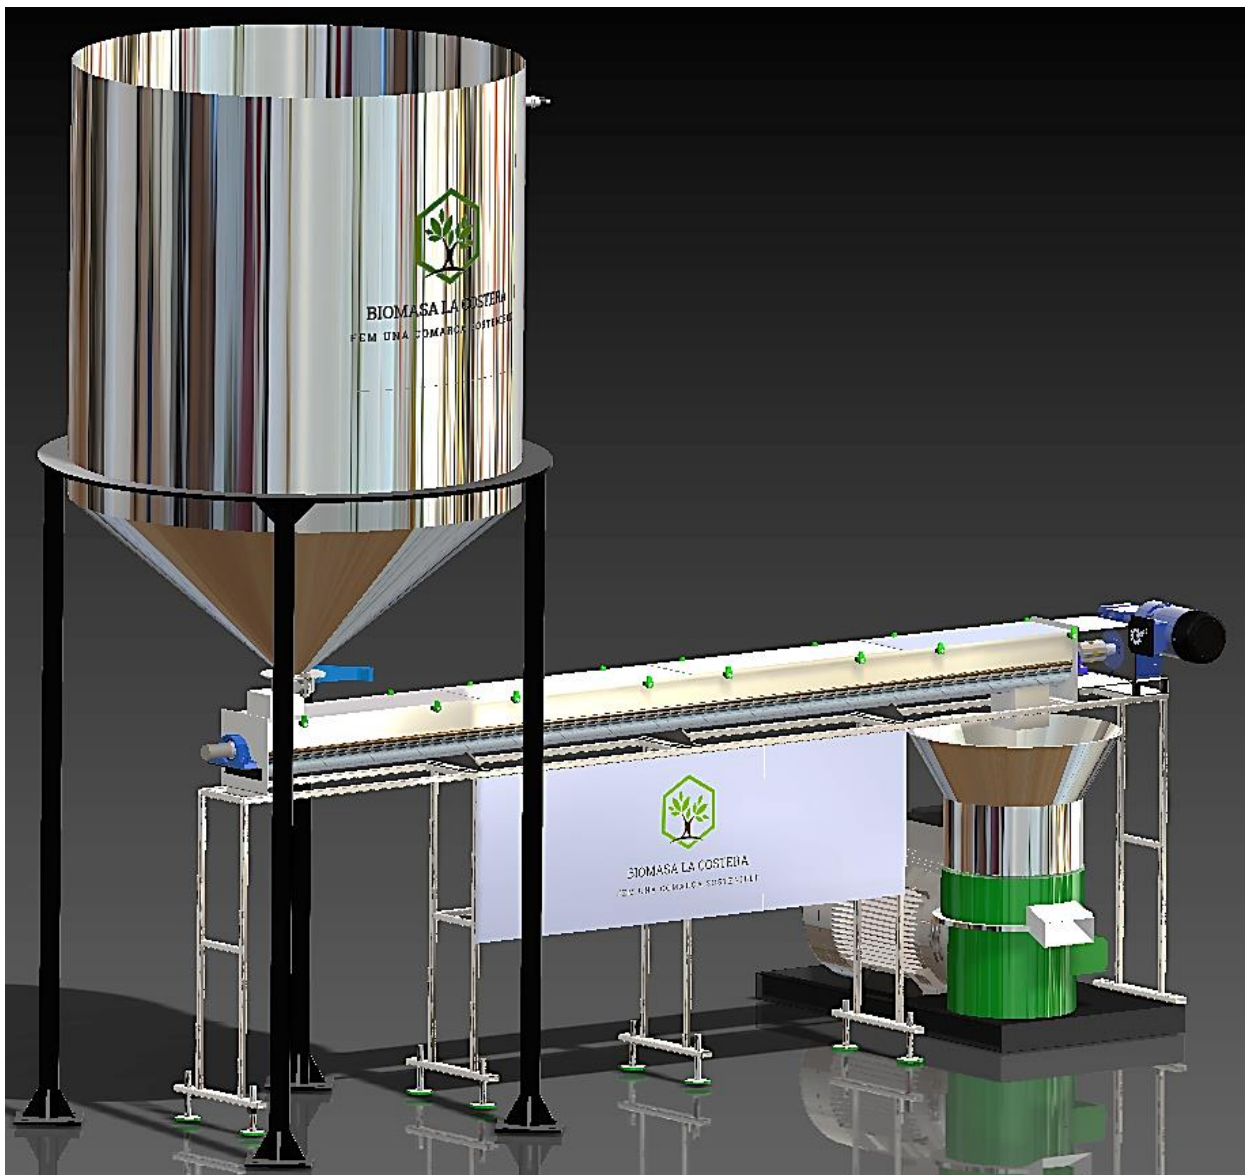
Diseño final en perspectiva (captura de solidworks assembly)
